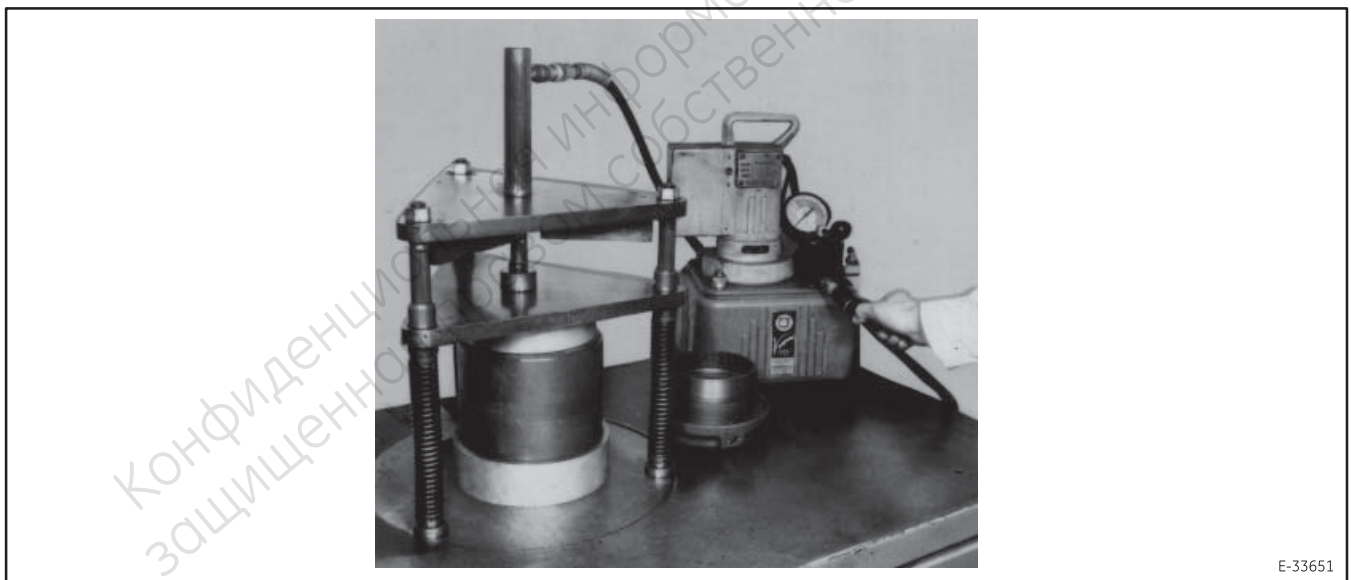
Запрессовка уплотнения в проточку наружного кольца подшипника.
